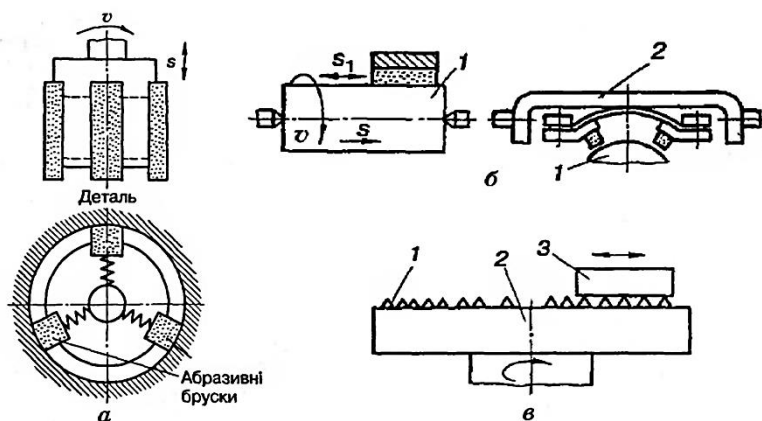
Схеми чистової обробки поверхонь: а) - хонінгування; б) - суперфініш; в) - притирання
